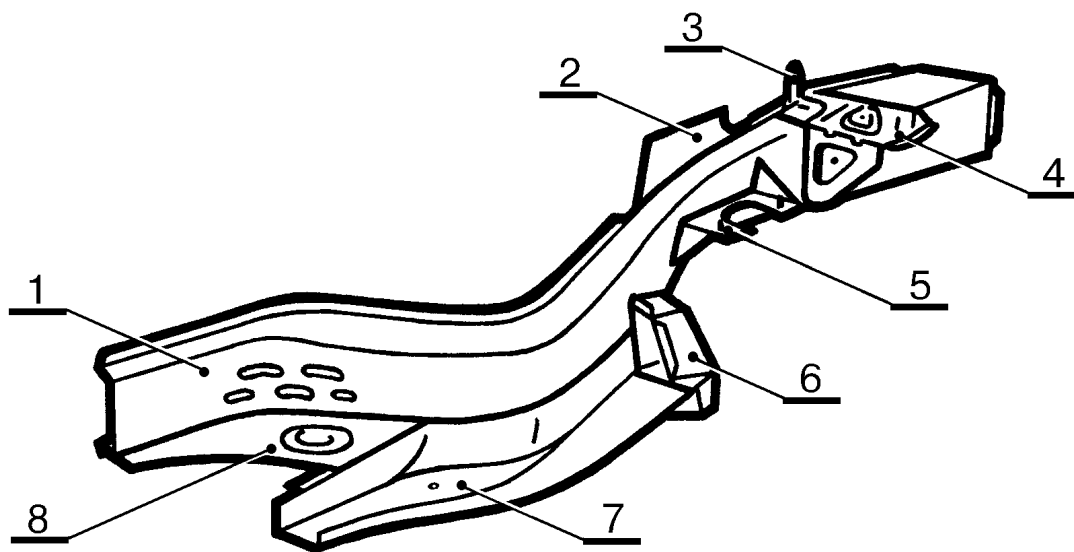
Детали лонжерона 2110-8403280/281 переднего с усилителем лонжерона, соединителем переднего лонжерона с полым и соединителем лонжерона со щитком передка в сборе. Номера и наименования деталей, количество и шаг сварочных точек приведены в таблице 17 (всего 28/66 точек).
